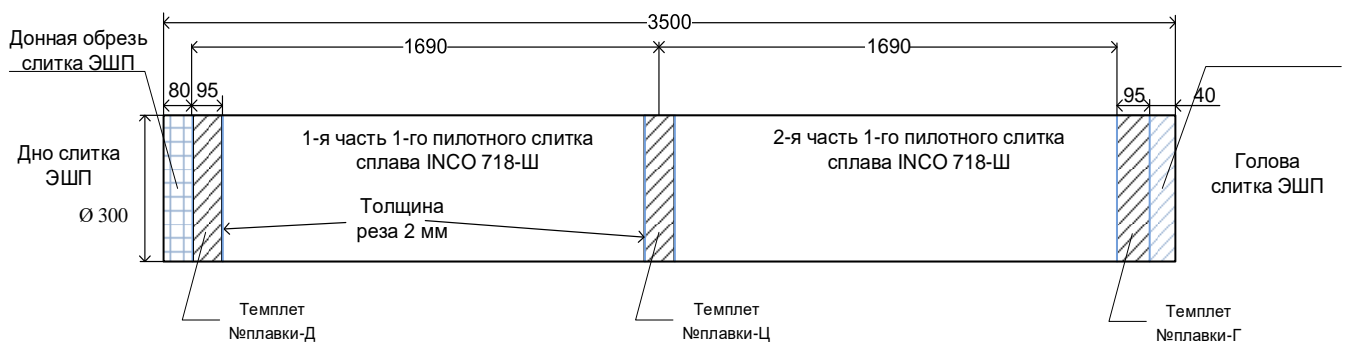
Схема порезки 1-го опытного слитка ЭШП сплава Inconel 718
